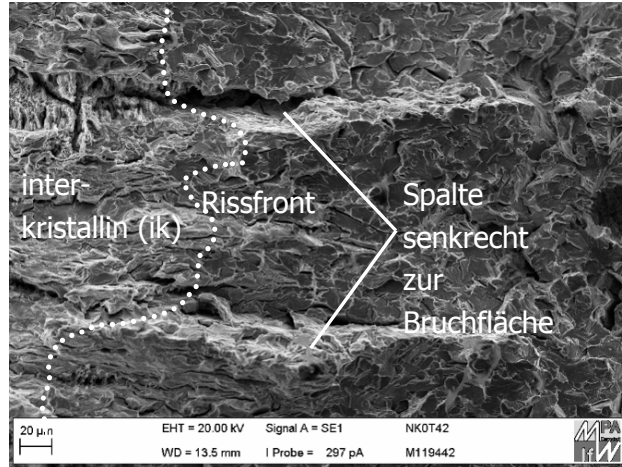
Detailbild aus Bild 6-24 Übergangsbereich ik <-> tk
